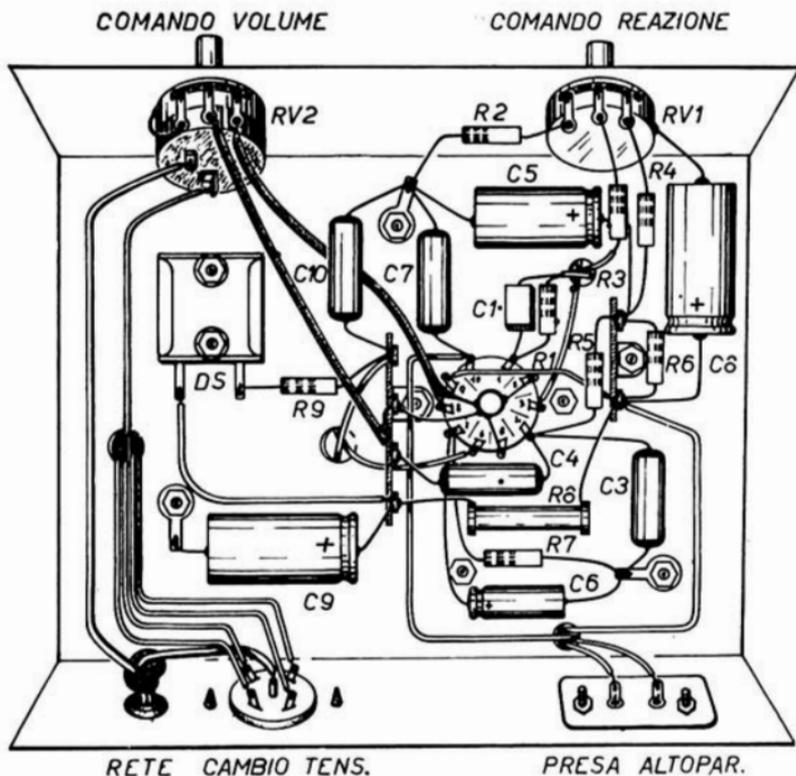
Componenti e collegamenti sotto il telaio.
